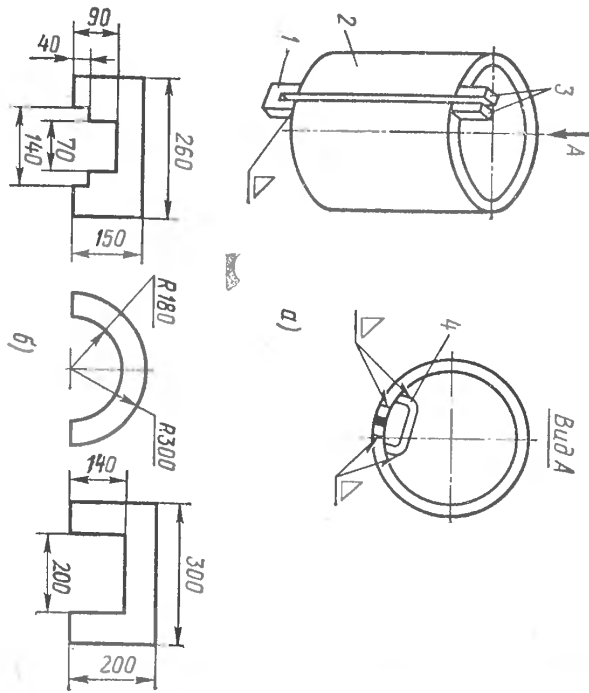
Подготовленная к электрошлаковой сварке заготовка в сборе (а) и виды скоб (б):
